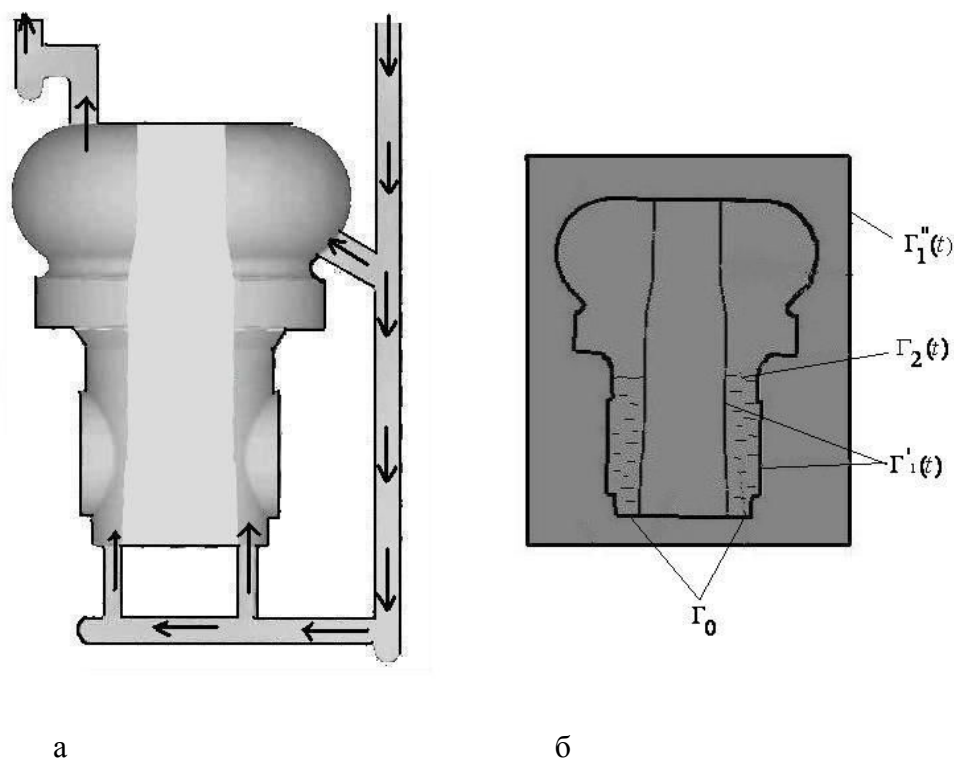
Форма для заливки превентора; а – схема движения расплава металла по форме, б – схема расчетной области – фронтальный разрез
